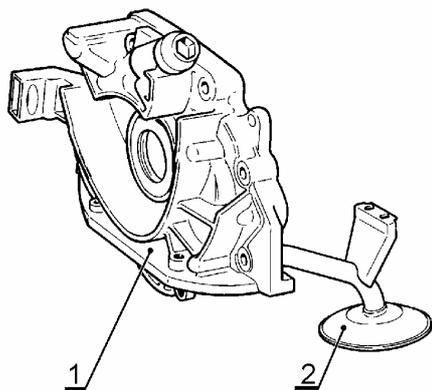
Насос масляный автомобилей двигателя ВАЗ-21114:
